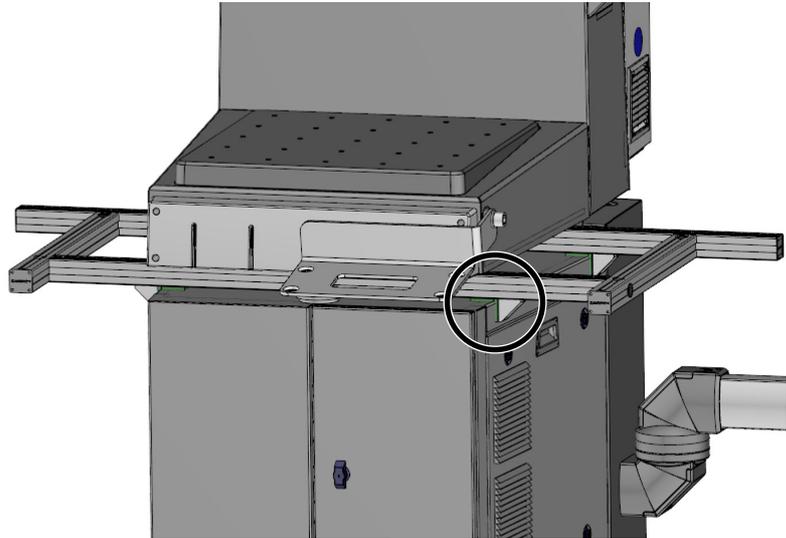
Rechte Befestigungswinkel anschrauben (Abbildung beispielhaft)
